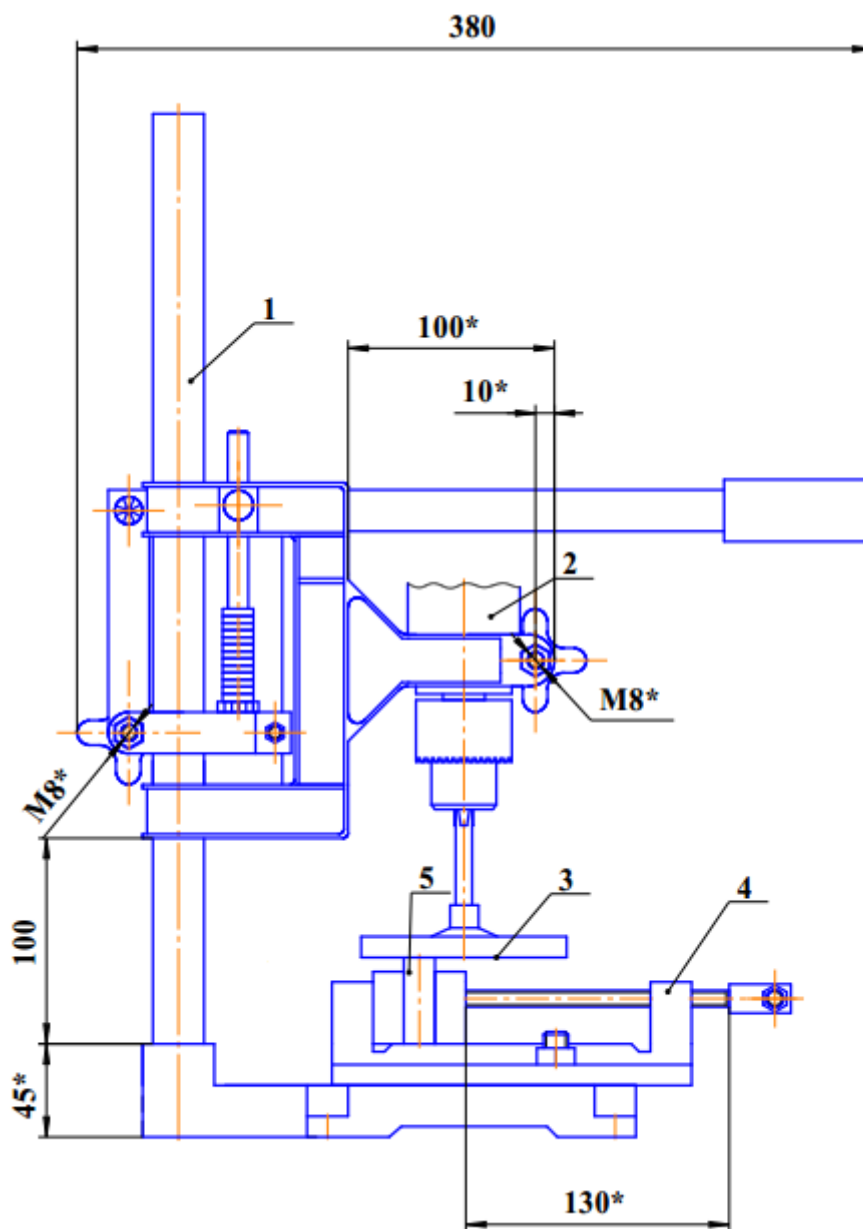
Установка для испытания износостойкости наплавленных образцов [14].
